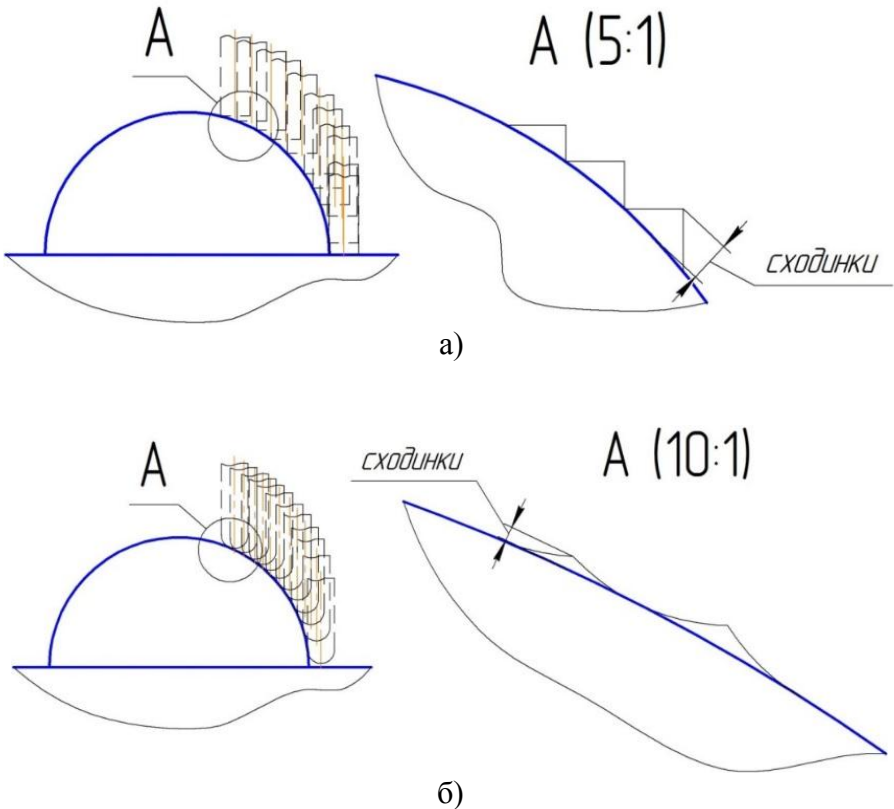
Макрорельєф сферичної поверхні під час оброблення: а) стандартною кінцевою фрезою; б) сферичною кінцевою фрезою
